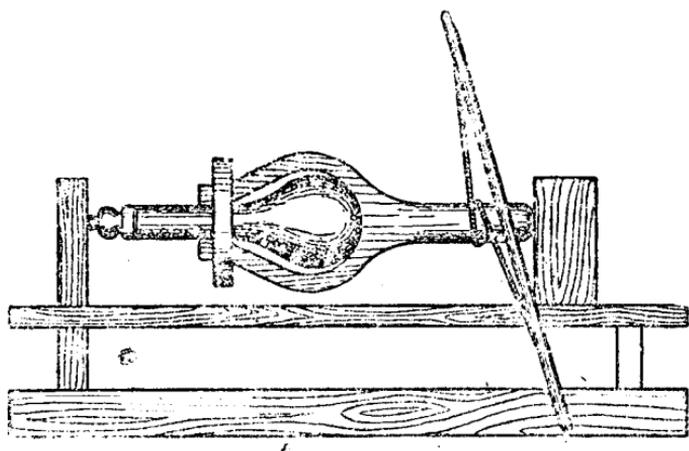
Простое настольное приспособление для затачивания черенка (смычковый токарный станок).
